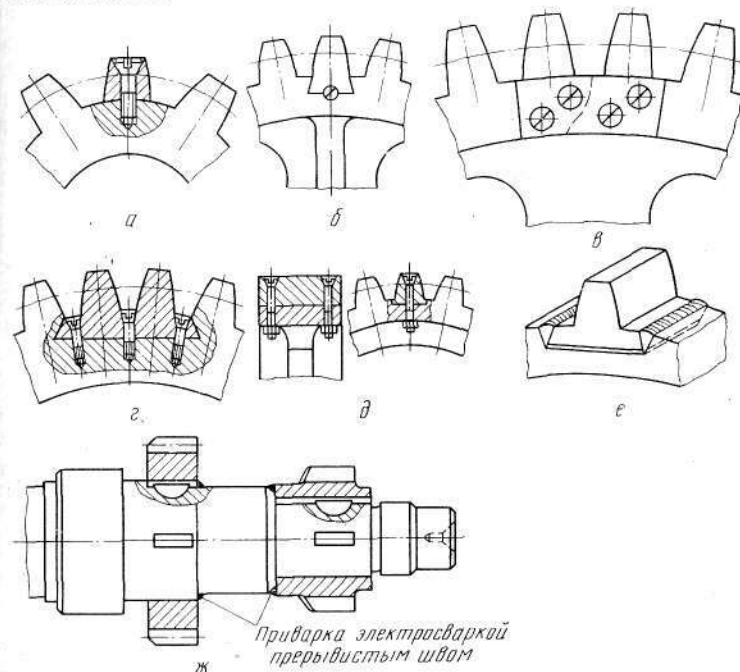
Способы ремонта зубчатых колес со сломанными зубьями
